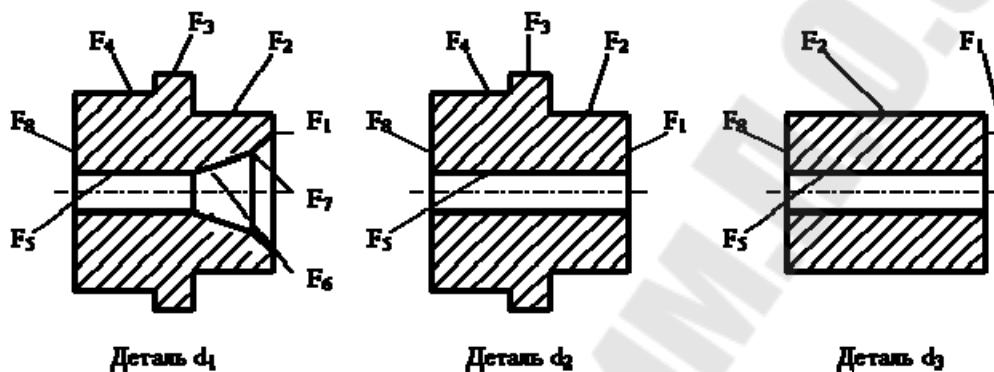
Эскизы деталей для обработки на прутковом токарном автомате
